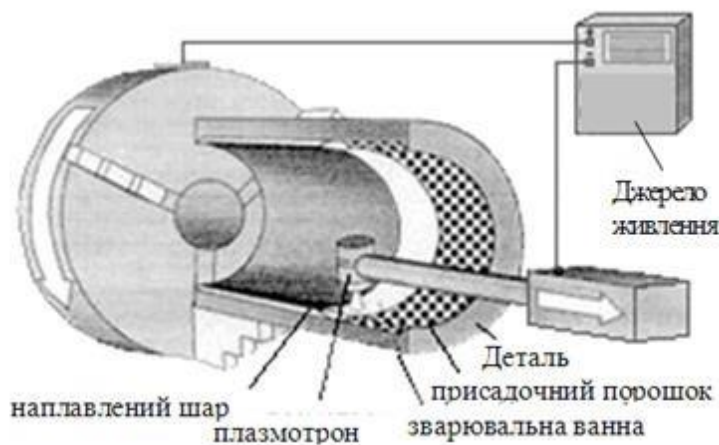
схема методу плазмового наплавлення [2]
